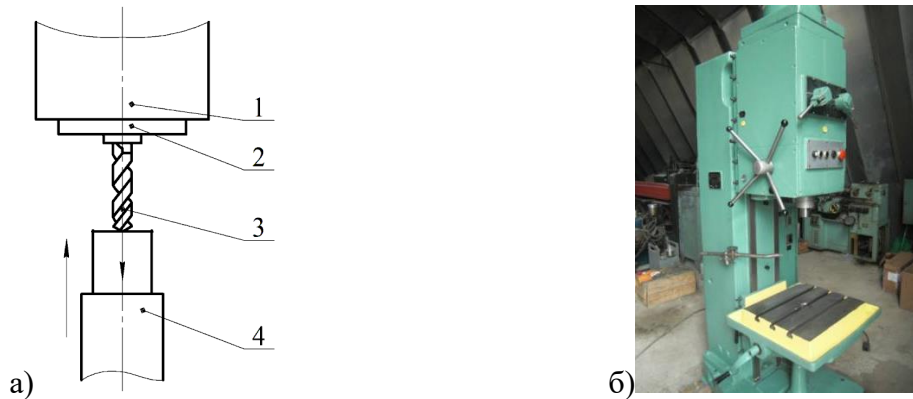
Дослідна установка – а) конструктивна схема; б) загальний вид: 1 – верстат; 2 – шпиндель; 3 – свердло; 4 – заготовка
